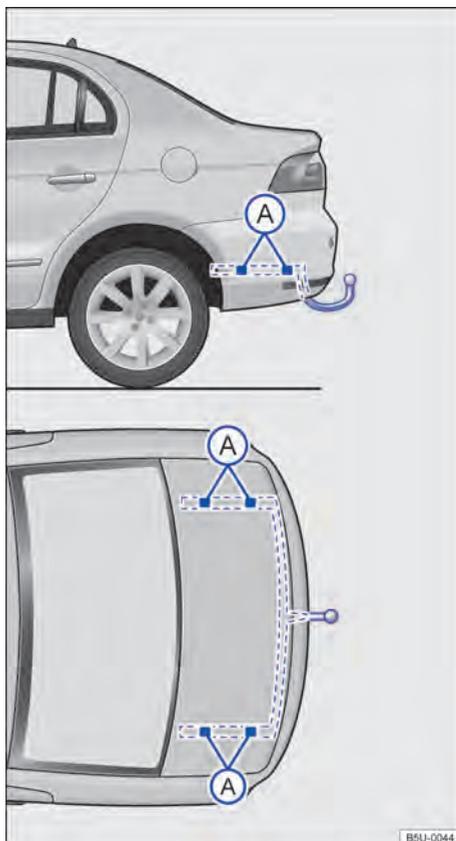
Pontos de fixação para instalar um dispositivo de reboque posteriormente.
